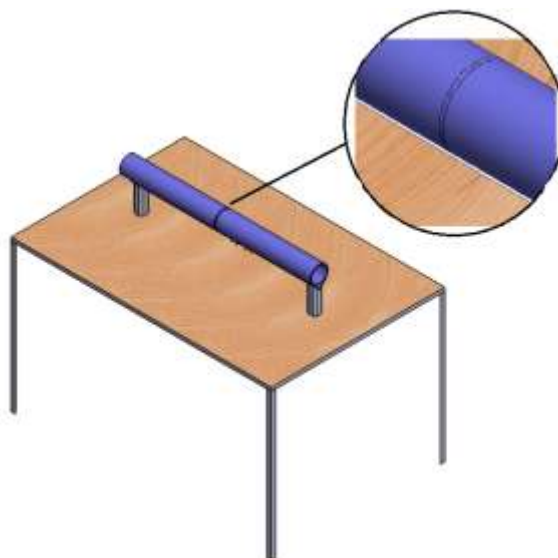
Figura II – Desenho em CAD da bancada para END com o tubo posicionado para inspeção.
